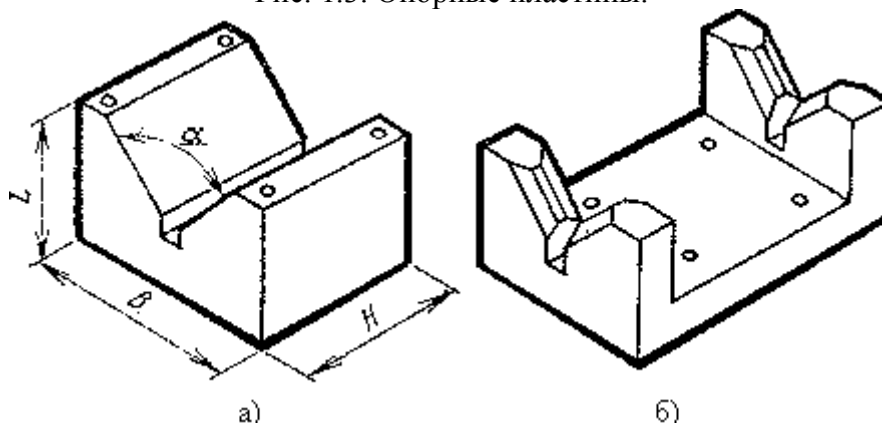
Элементы для установки заготовок по наружным и внутренним цилиндрическим поверхностям: а, б – призмы широкая и узкая сдвоенная.
